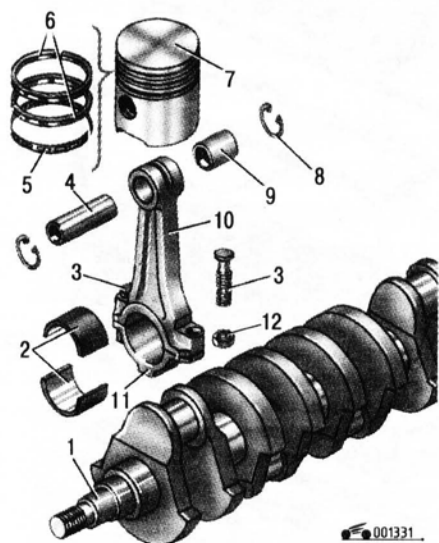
Коленчатый вал и детали шатунно-поршневой группы: 1 – коленчатый вал; 2 – вкладыш шатунного подшипника; 3 – болт крепления крышки шатуна; 4 – поршневой палец; 5 – маслосъемное кольцо; 6 – компрессионные кольца; 7 – поршень; 8 – стопорное кольцо; 9 – втулка головки шатуна; 10 – шатун; 11 – крышка шатуна; 12 – гайка крепления крышки шатуна
